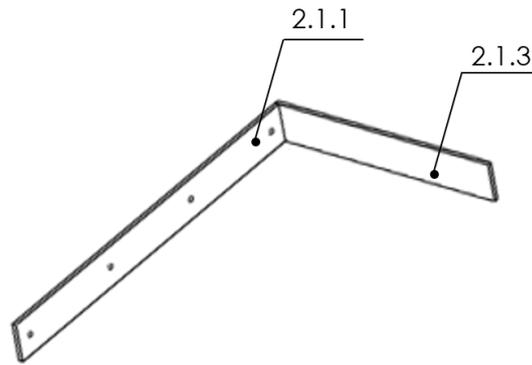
Ensamblaje subconjunto 2.1 mesa de centro. Soldadura 1
